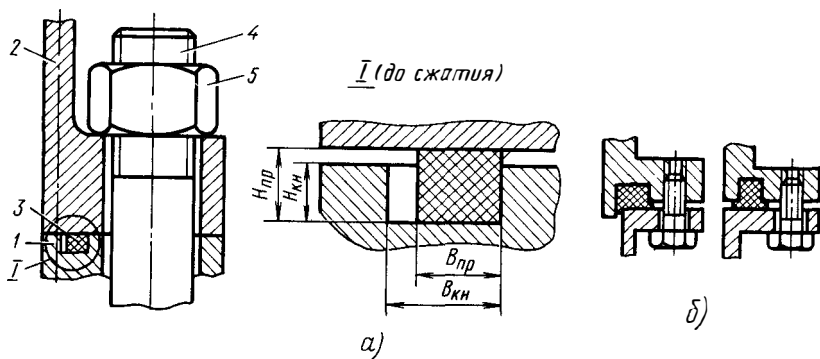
Герметизация корпуса блока с помощью резиновой уплотнительной прокладки:
